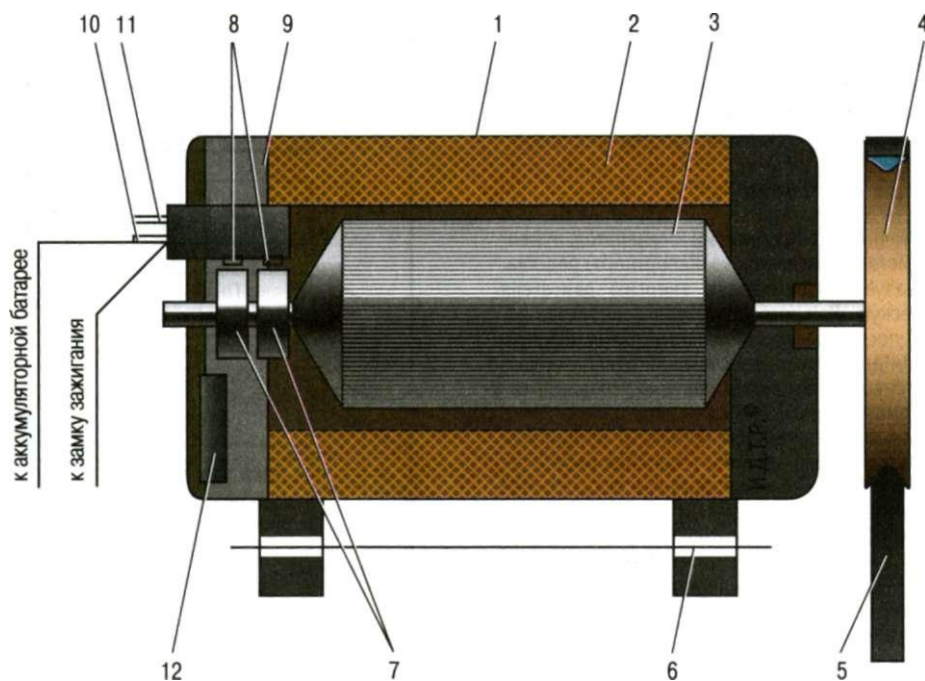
Устройство генератора: 1 - корпус генератора; 2 - обмотка статора; 3 - ротор; 4 - шкив привода генератора; 5 - ремень; 6 - кронштейн крепления; 7 - контактные кольца; 8 - щетки; 9 - регулятор напряжения; 10 - вывод «30» для подключения потребителей; 11 - вывод «61» для питания цепи амперметра и контрольных ламп на щитке приборов; 12 - выпрямитель
